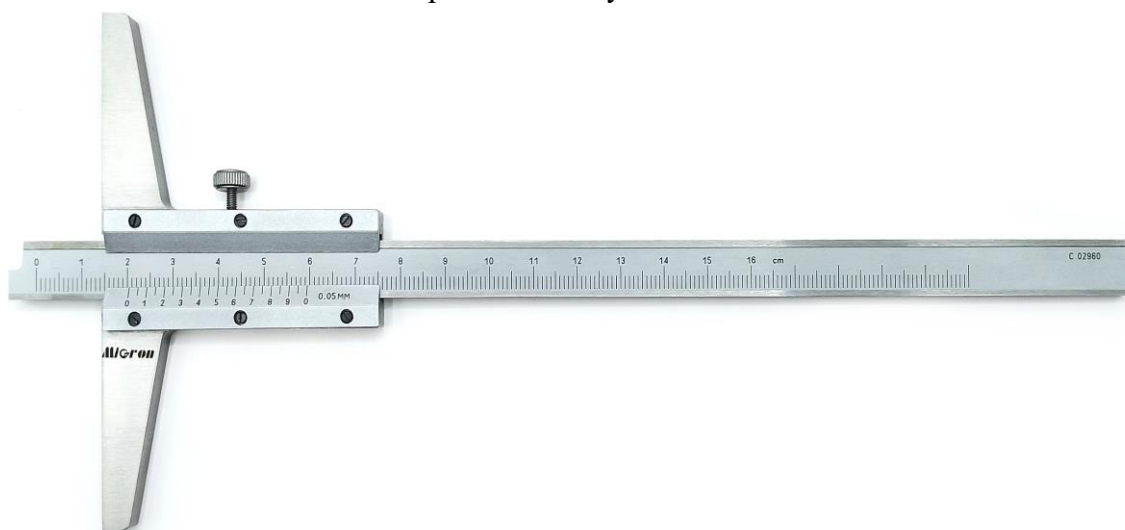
Общий вид штангенглубиномеров модификации ШГ со ступенчатым краем штанги
